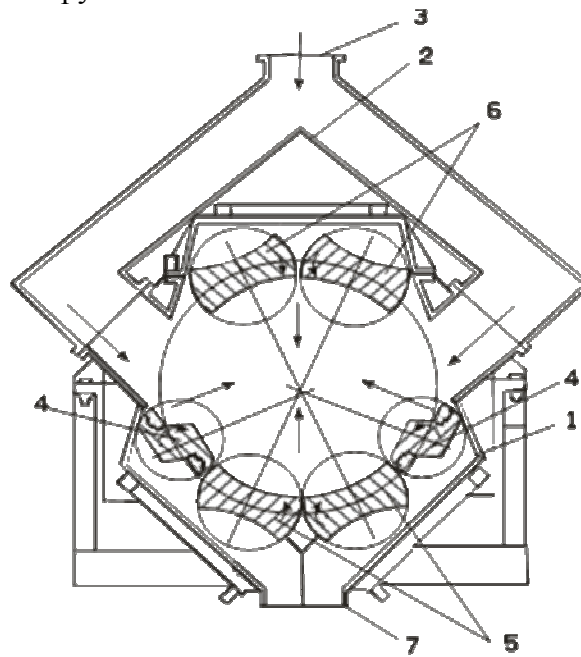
Схематическая конструкция дробилки ДКД-300: 1 – корпус дробилки; 2 – делитель потока; 3 – загрузочный патрубок; 4 – первичные ротора; 5 – нижняя пара роторов; 6 – верхняя пара роторов; 7 – разгрузочный патрубок
